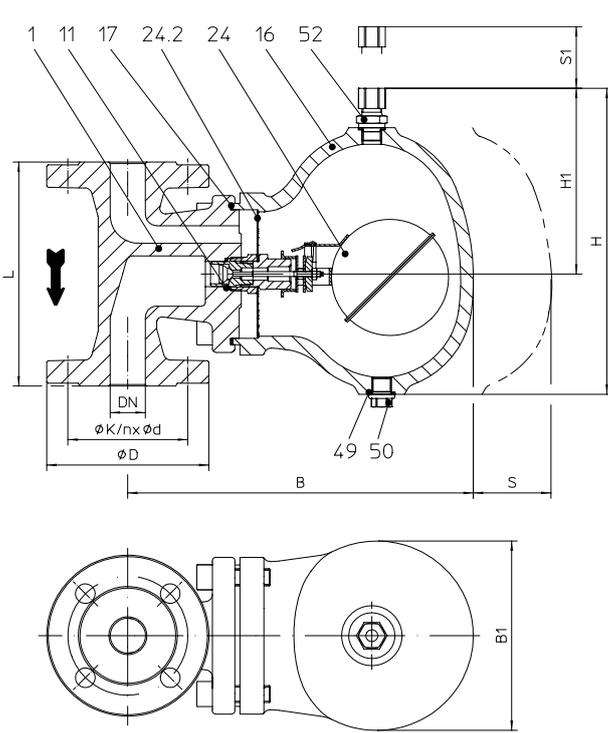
1 mit Flanschen - vertikale Einbaulage
